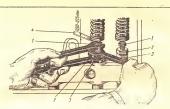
Регулировка зазора с нижним расположением клапанов; 1 — регулировочный винт; 2 — контргайка; 3 — толкатель; 4 — щуп,
